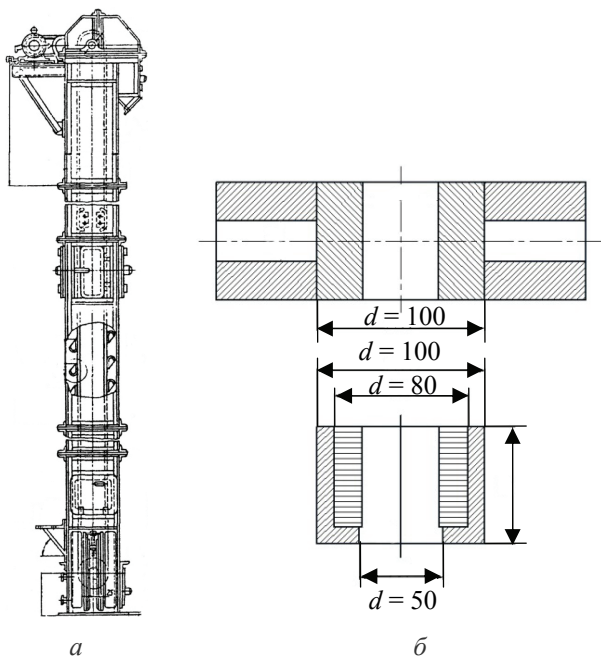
Эlevator (а) для подачи песка в сушильные барабаны и самосмазывающийся подшипник скольжения (б) нижней головки элеватора
